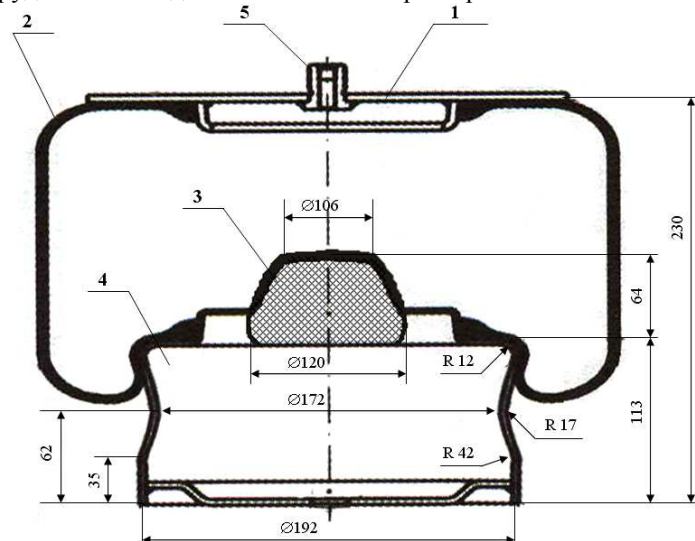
Вид рукавного пневматического элемента Taurus 370-230 в разрезе.
